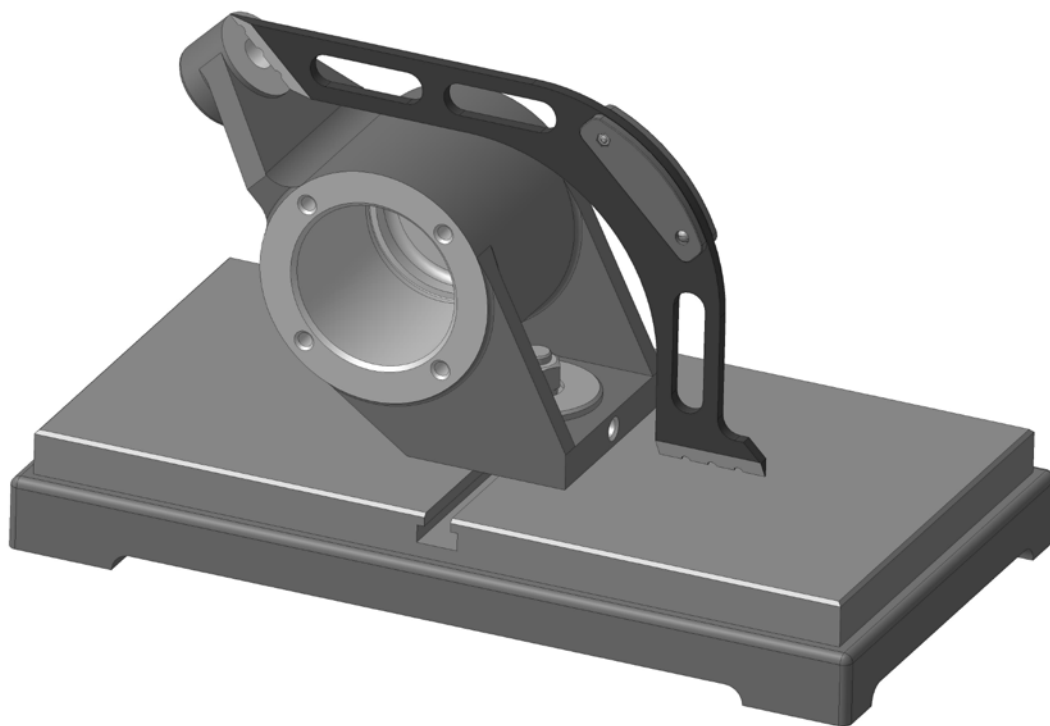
Схема крепления детали в приспособлении и контроля угла наклона
